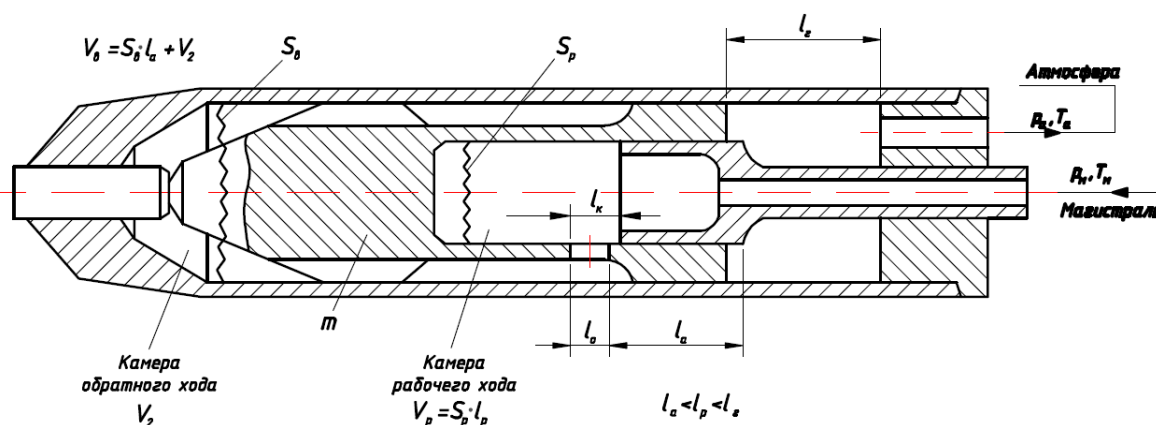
Схема пневмоударного устройства с одной управляемой камерой
